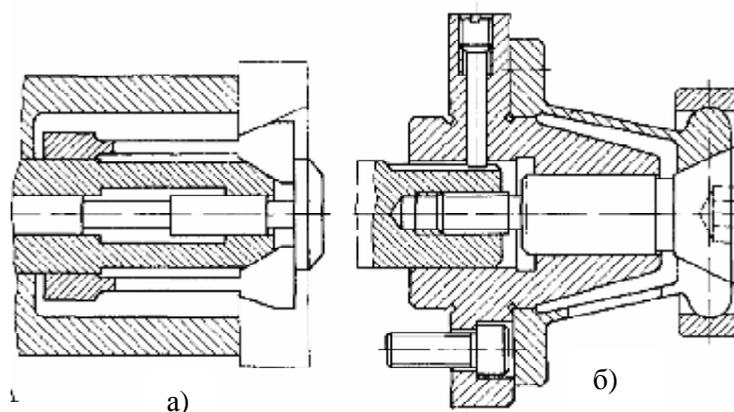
Цанговые оправки для установки заготовки по конической поверхности (а) и по фасонной поверхности (б)
